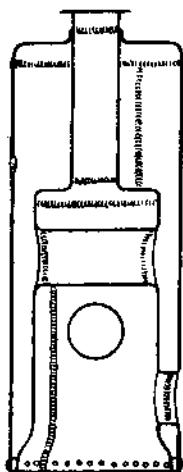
Вертикальный паровой котел, изготовленный по-средством автогенной сварки.
